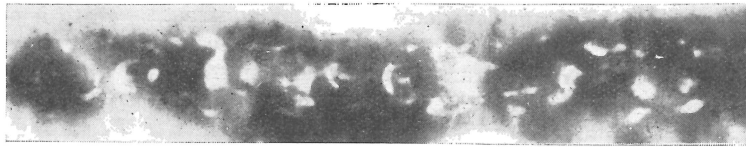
Radiographie d'une soudure en X (tôle de 20 mm) : très nombreuses inclusions de laitier.
